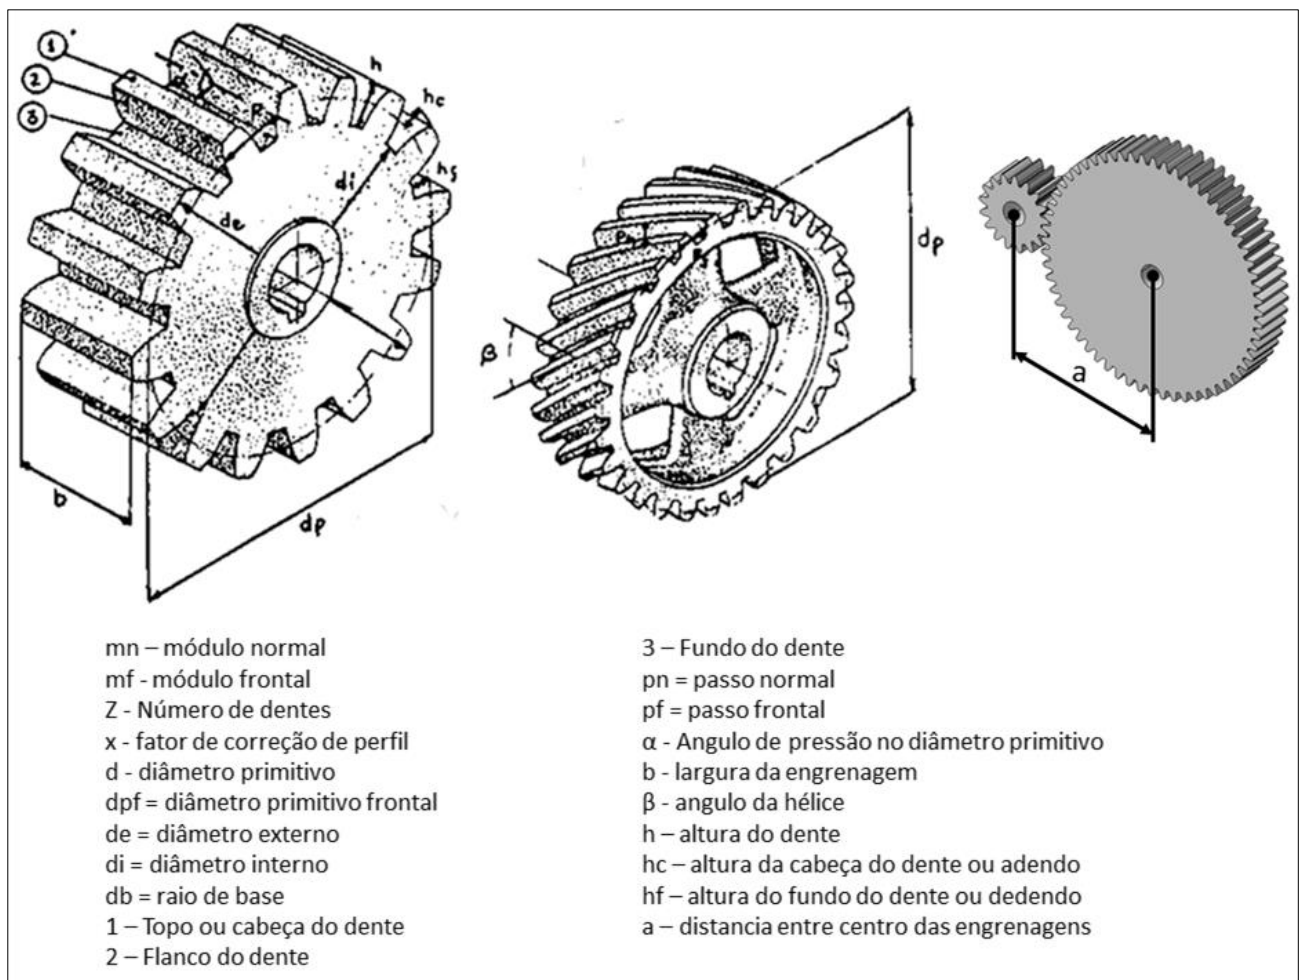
Engrenagem cilíndrica reta e helicoidal.
